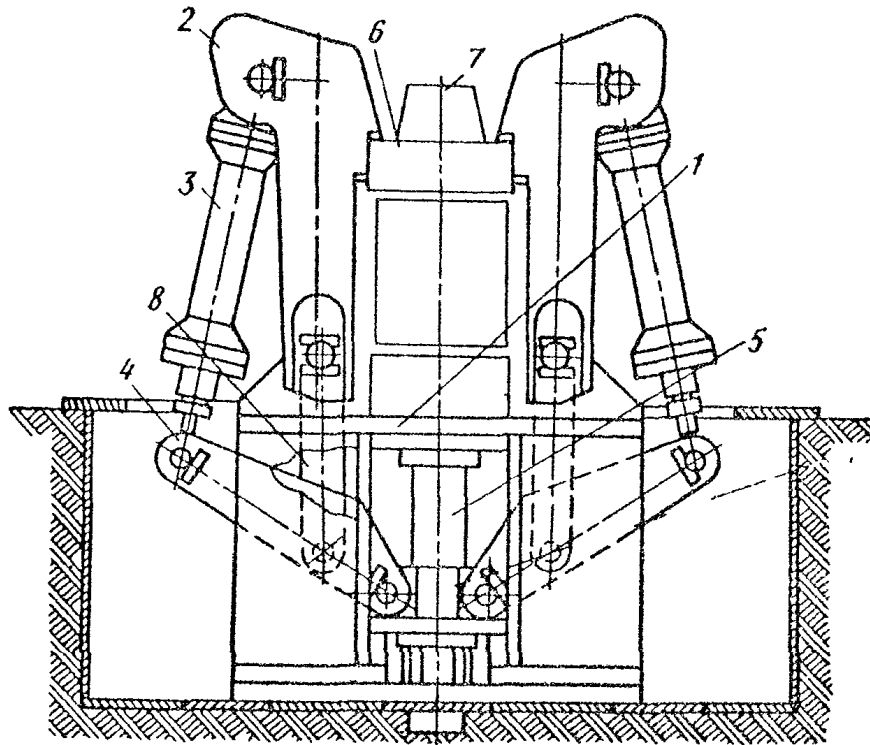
Пристрій для виштовхування злитка з виливниці
